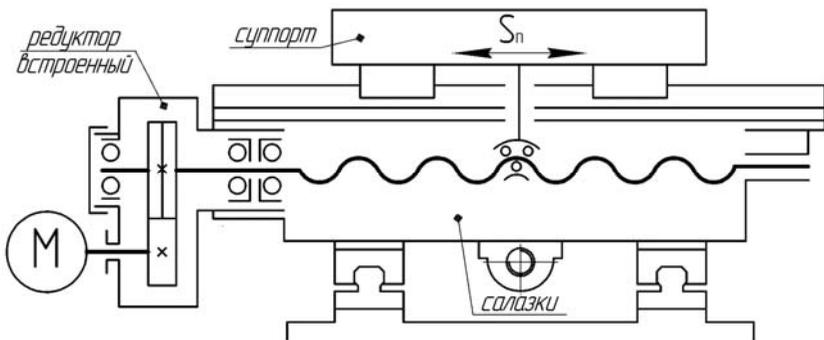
Структурно-кинематическая схема автономного привода поперечной подачи суппорта  $s_n$  со встроенным механическим редуктором и бесступенчатым регулированием токарного станка с ЧПУ
